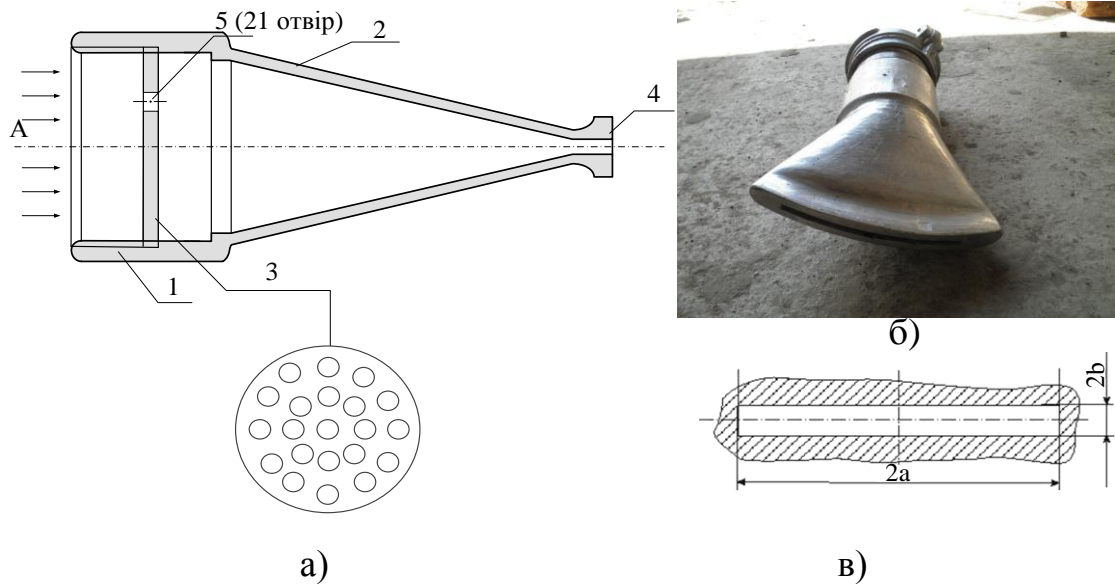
Загальний вигляд конструкції і схеми елементів насадка для створення плоско-радіального струменя
